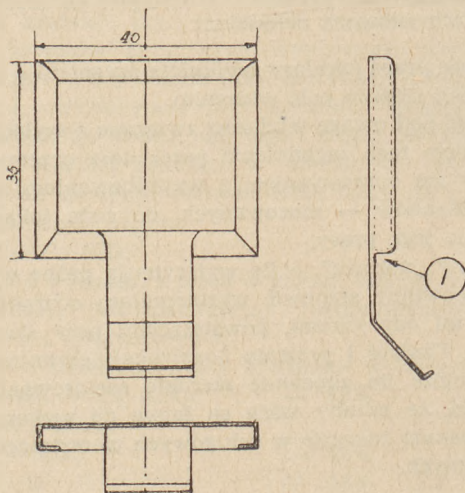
Ekran nożowy typu A i B z szybkami szklanymi. niżej. Pierwsze badania prowadzone były nad prototypami ekranów typu A, następnie przebadano ekrany typu B.
